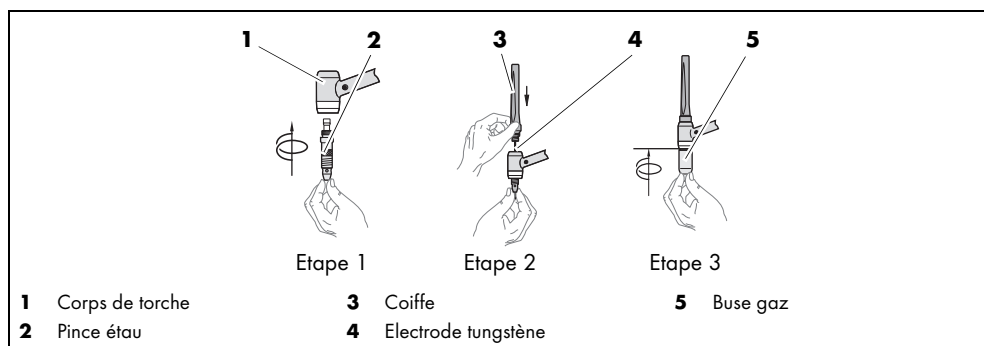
Torche de soudage ABITIG® Little 24G, 24W, 9, 17, 25
